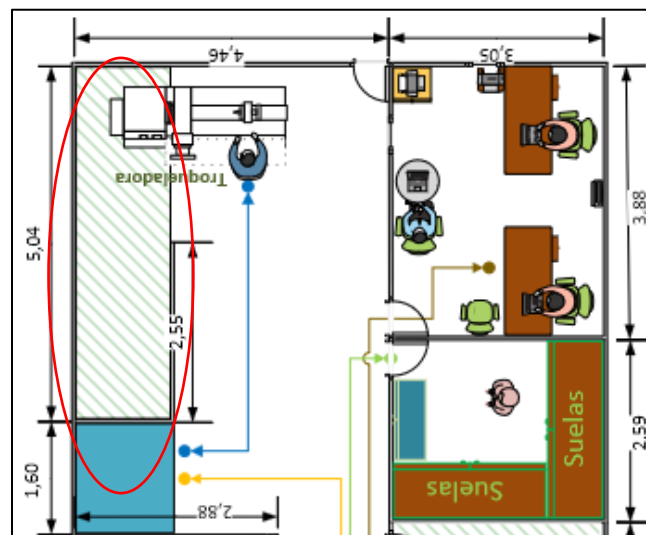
Zona de almacenamiento de materia prima en el primer piso de la planta
